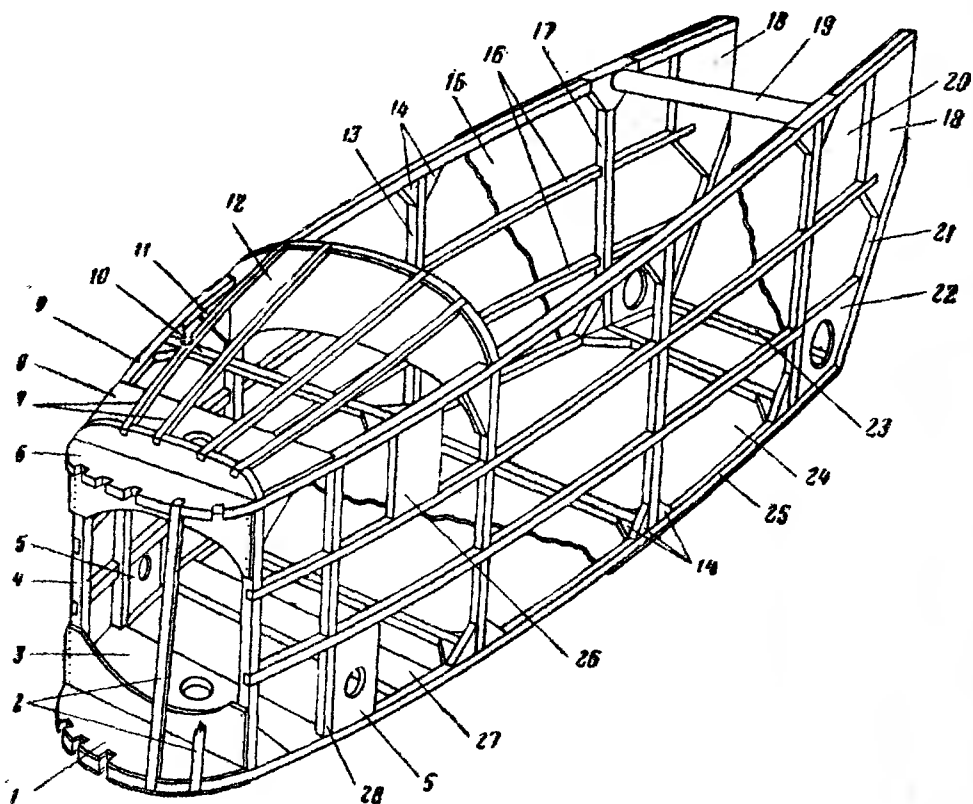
Каркас корпуса полужакрытых аэросаней «ОСГА-4»: 1, 6 — профилированные бобышки носовой части; 2 — стойки; 3 — усиление пола; 4 — шпангоут № 1; 5 — заполнение для оси педалей; 7 — рейки; 8 — заполнение; 9 — верхний силовой стрингер; 10 — поперечная рейка для оси рулевого управления; 11, 26 — заполнение для крепления роликов троса управления; 12 — шпангоут № 3; 13 — шпангоут № 4; 14 — угловые бобышки; 15 — наружная обшивка; 16 — стрингеры; 17 — шпангоут № 5; 18 — заполнение для крепления двигателя; 19 — трубчатая распорка; 20 — внутренняя обшивка; 21 — укосица; 22 — заполнение для оси задней подвески; 23 — поперечная рейка; 24 — обшивка днища; 25 — нижний силовой стрингер; 27 — поперечная доска для установки педалей; 28 — шпангоут № 2.
